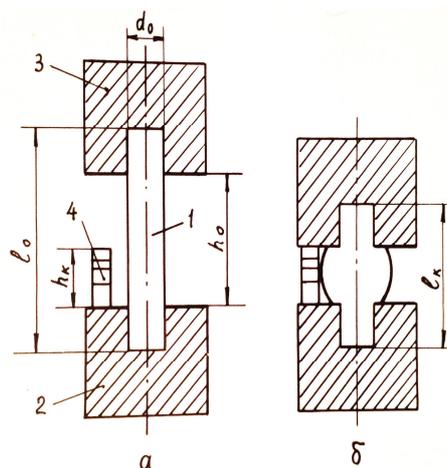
Схема деформирования заготовок для изготовления ударных образцов
